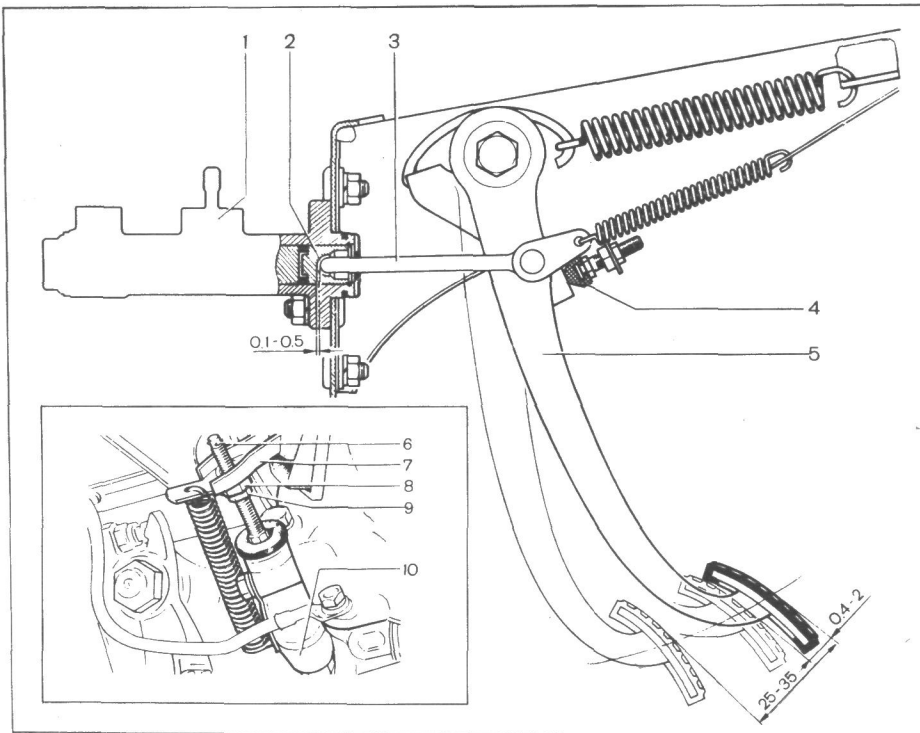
Регулировка привода выключения сцепления: 1 — главный цилиндр сцепления; 2 — поршень; 3 — толкатель; 4 — ограничитель; 5 — педаль сцепления; 6 — толкатель рабочего цилиндра; 7 — вилка выключения сцепления; 8 — гайка; 9 — контргайка; 10 — рабочий цилиндр
